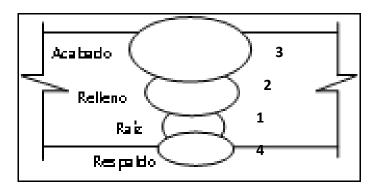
Secuencia de soldadura y número de capas de soldadura
